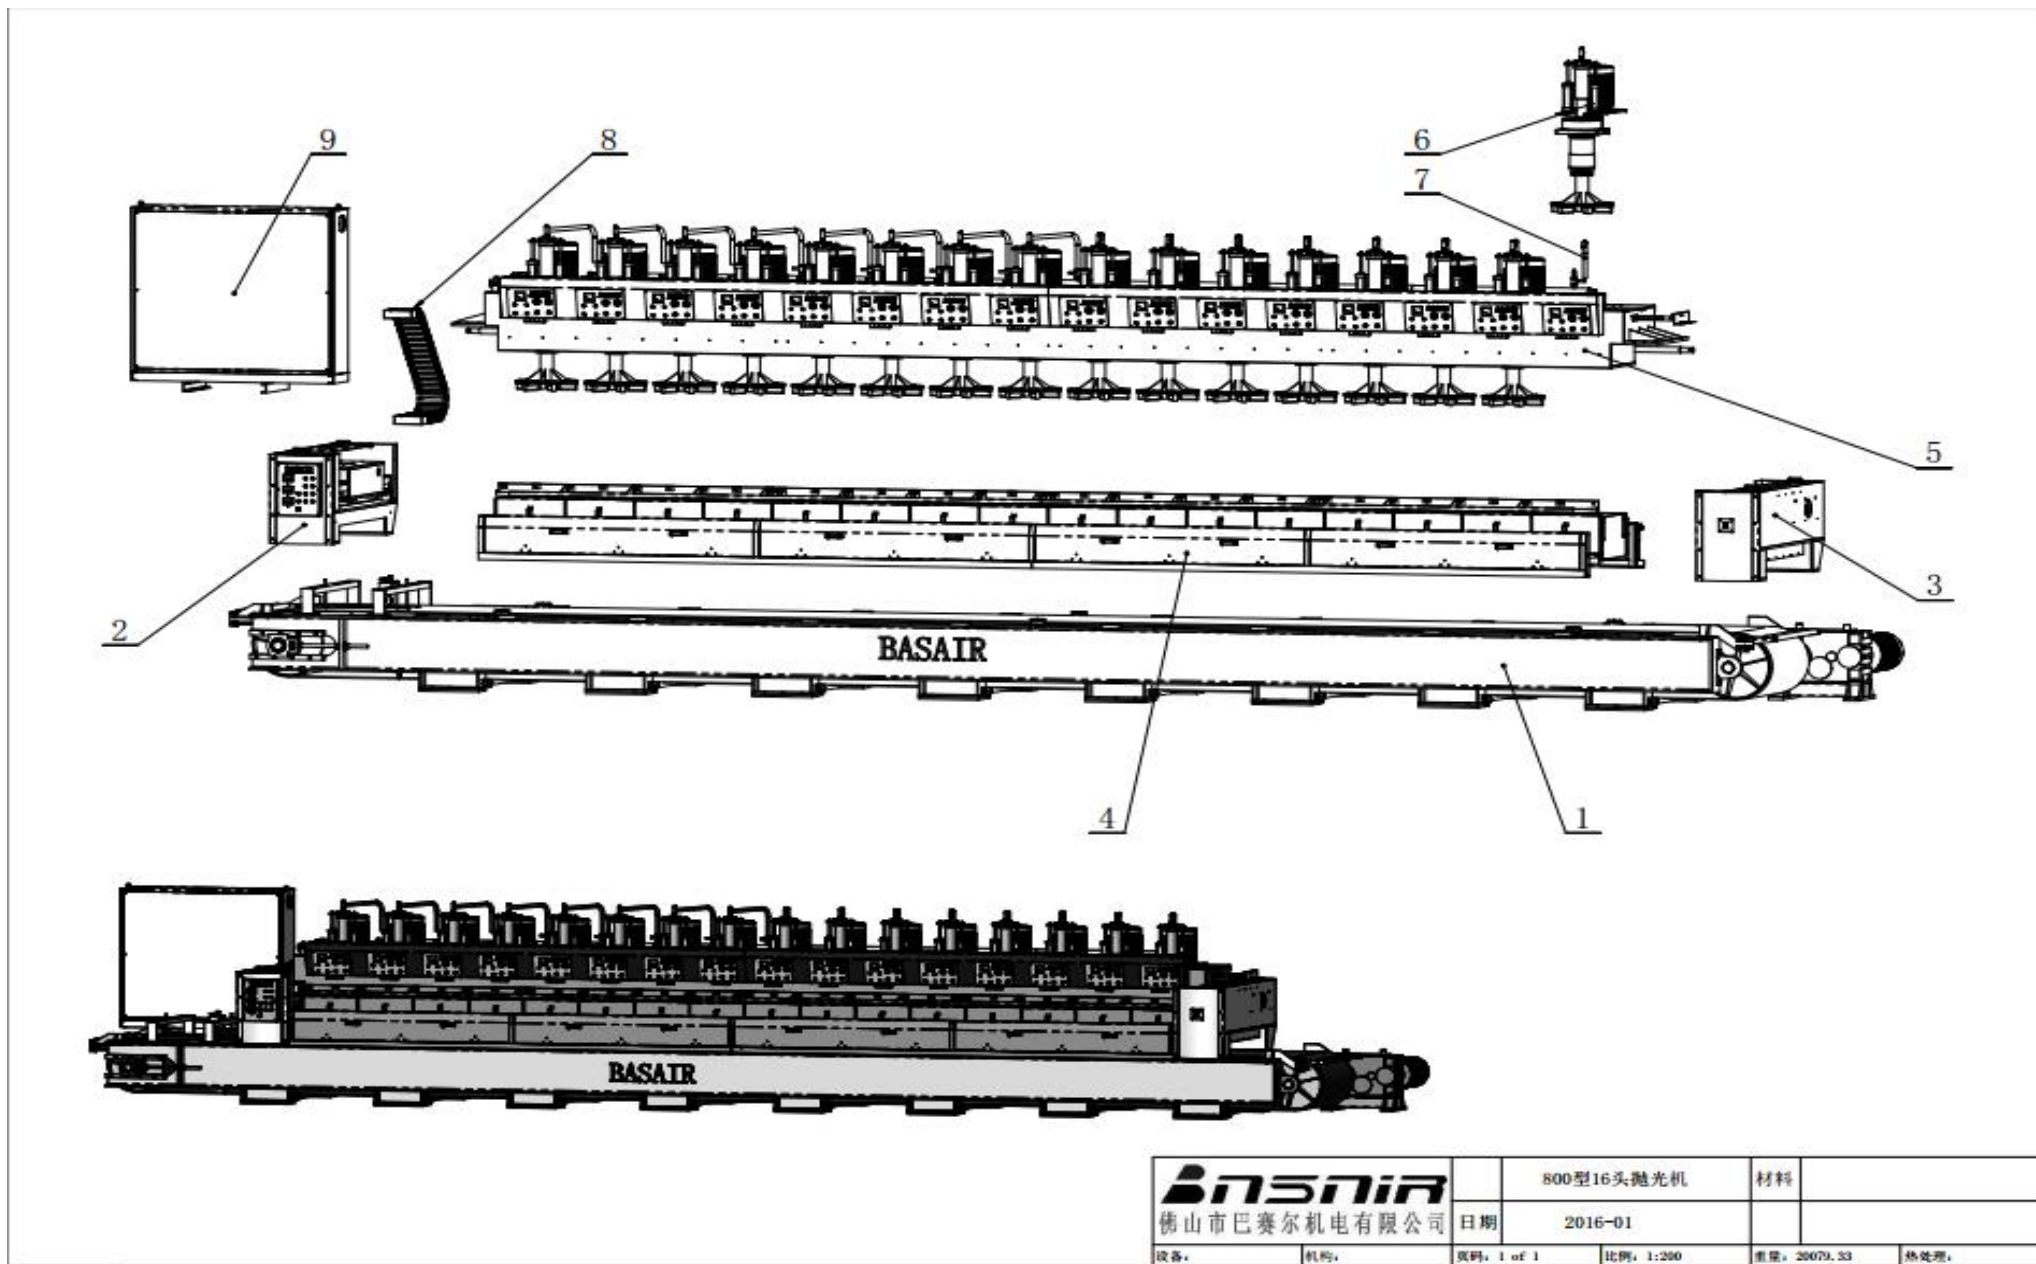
BP1000/16 抛光机 总图 picture1 BP1200/16 polishing machine general drawing
